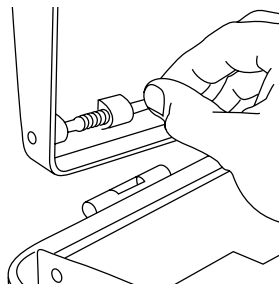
Detail zapojení1. Instalace ovládací jednotky SL4800
